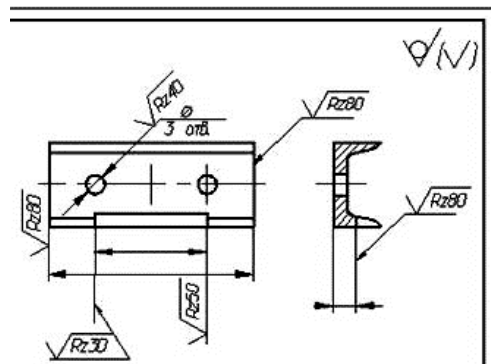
Пример обозначение шероховатости поверхностей повторяющихся элементов изделия
